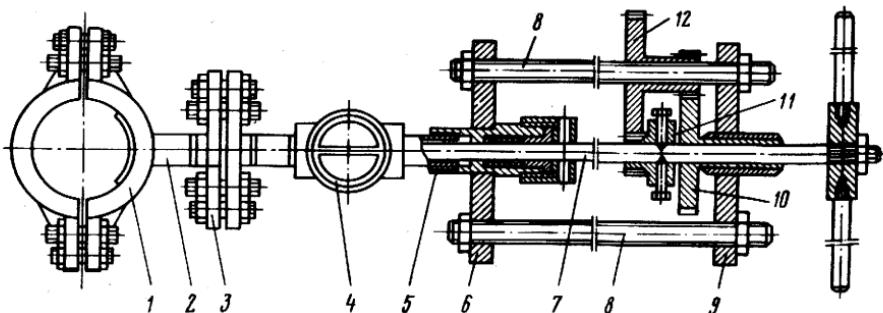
Приспособление для сверления труб под давлением с автоматической подачей сверла
